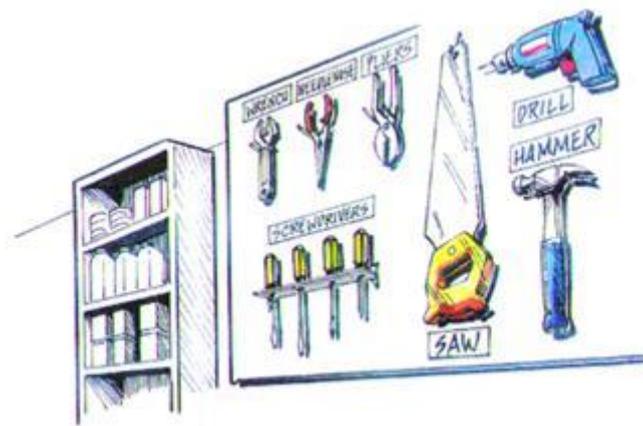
Exemplar einer geordneten Werkzeugwand³³
